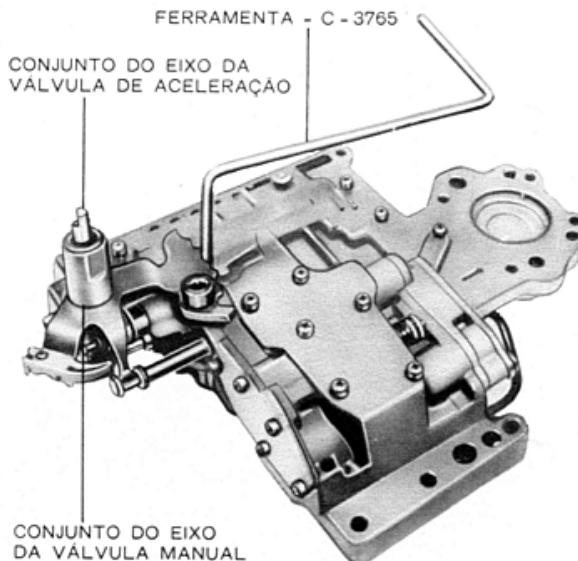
Instalação da esfera limitadora, mola e alavancas de controle
